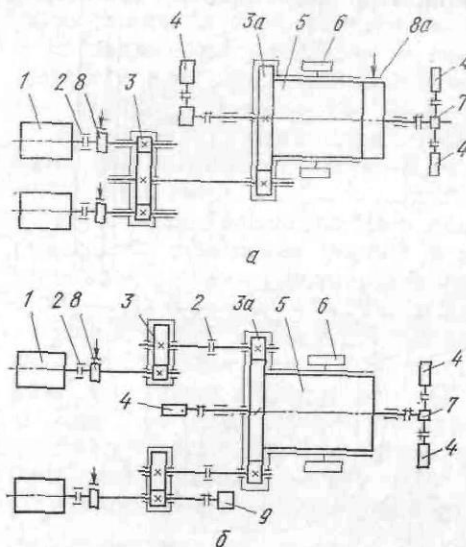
Кинематические схемы скиповых лебедок: а — с общим редуктором; б — с отдельными редукторами
